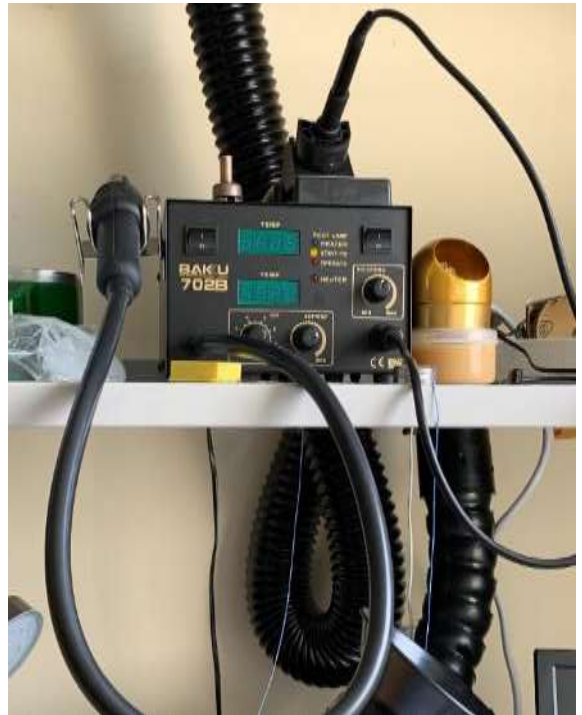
、84:電子顯微鏡與 BAKU 702B 焊接站，可焊接維修手機主機板等物
